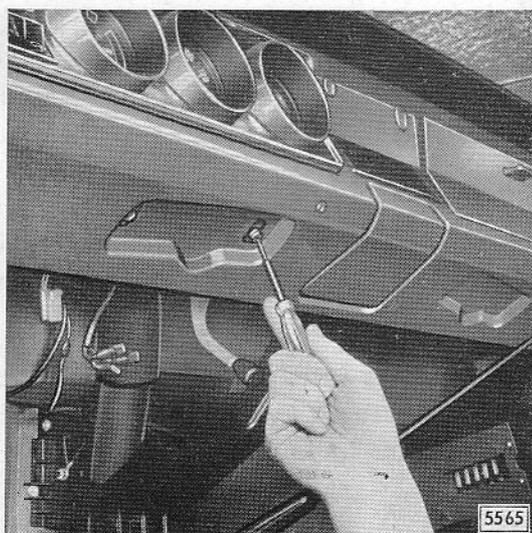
Schraubenschraube aus Haltestrebe herausschrauben
